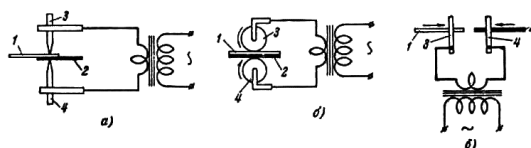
Виды электроконтактной сварки: а) — точечная, б) — роликовая, в) — стыковая; 1, 2 — свариваемые детали; 3, 4 — электроды
